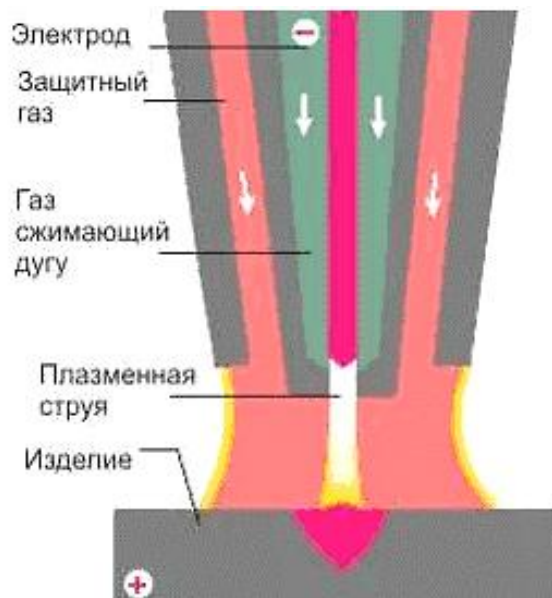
Схема процесса плазменной сварки неплавящимся электродом на прямой полярности
